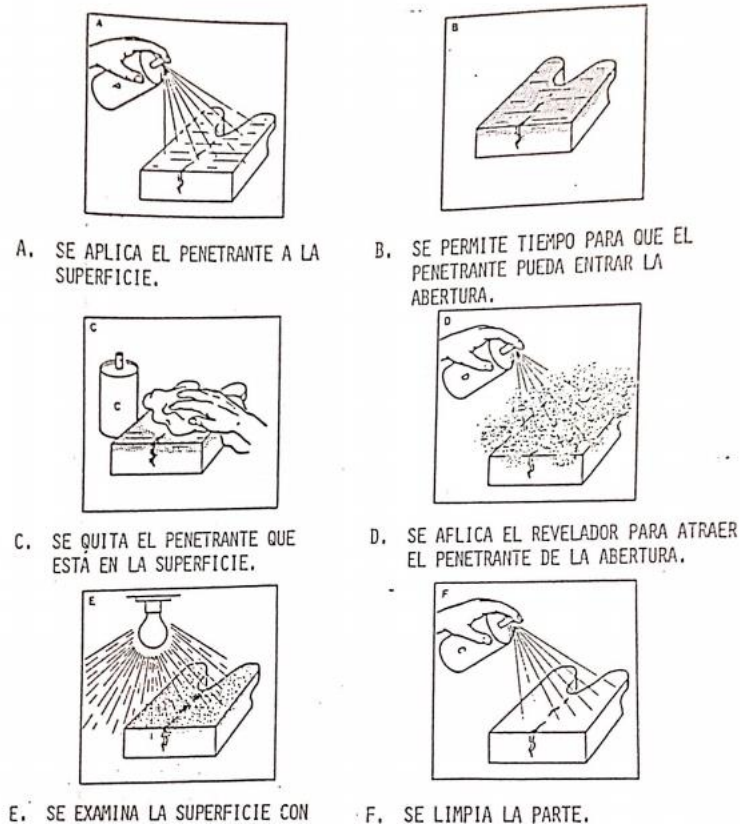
Secuencia de inspección con líquidos penetrantes.
